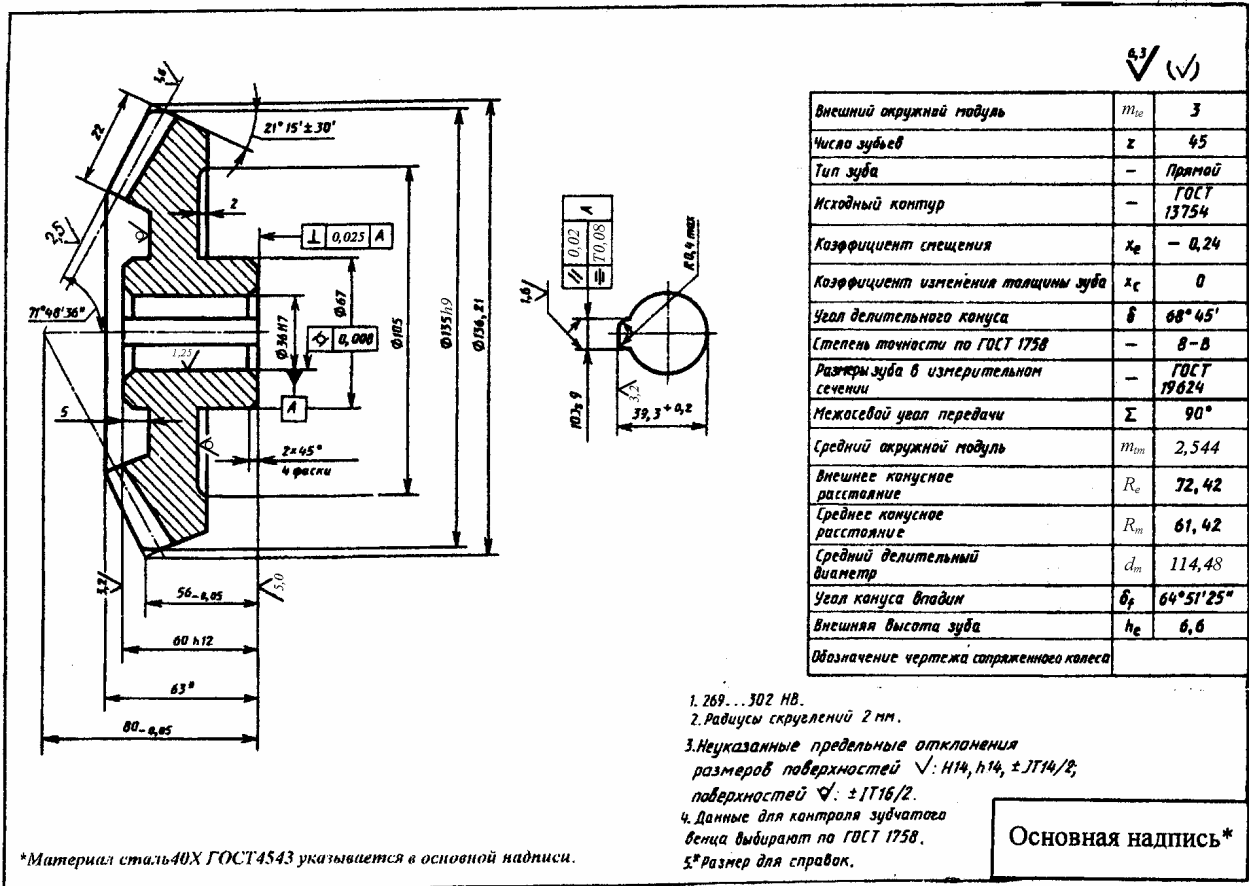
Рабочий чертеж конического прямозубого колеса
